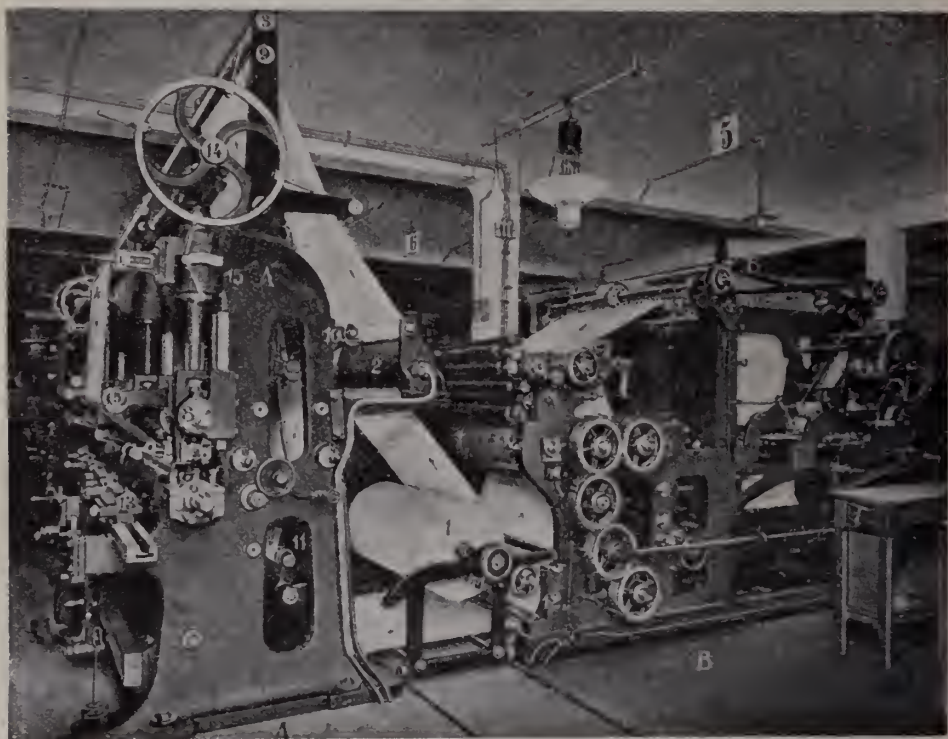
Kupferdruckmaschine in Verbindung mit einer Buchdruck-Rotationsmaschine für Mertensdruck (1910). — Tiefdruckanlage des „Hamburger Fremdenblattes“.
